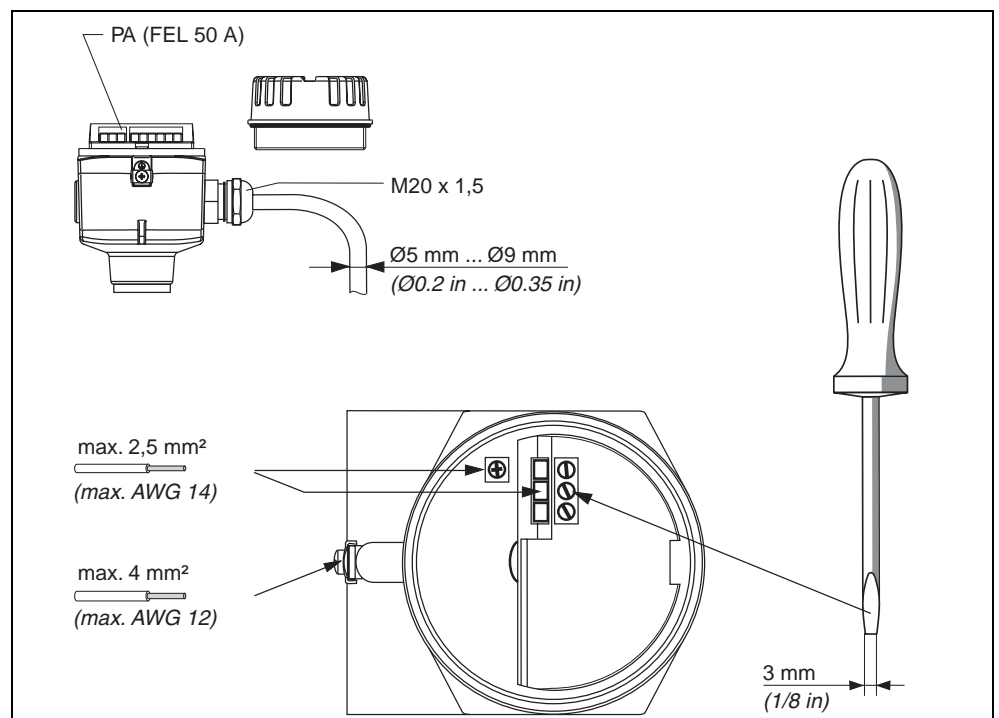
Anschließen des Messumformers mit Kabelverschraubung
